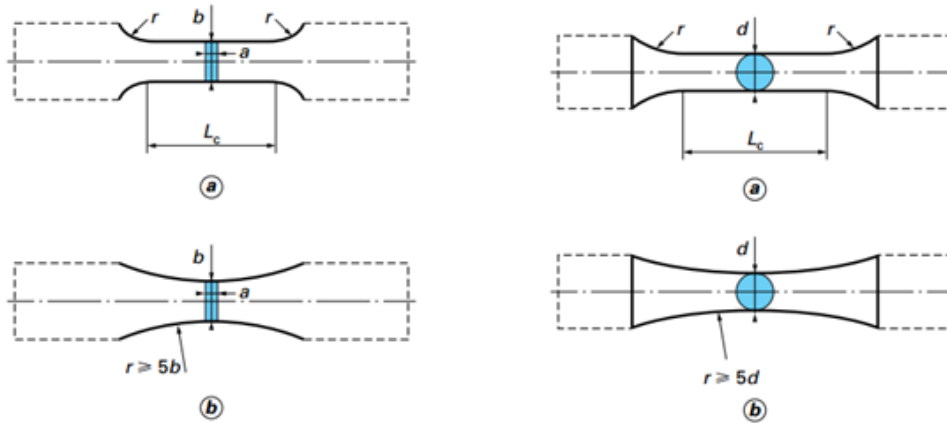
1 Éprouvettes parallélépipédiques à section rectangulaire et éprouvettes axisymétriques à section circulaire [6]
